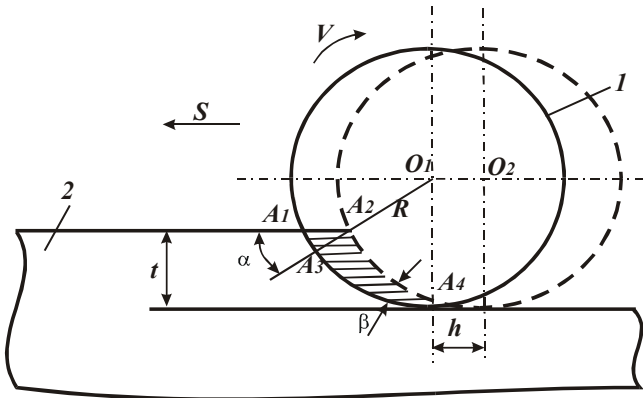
Розрахункова схема параметрів циліндричного фрезерування:
